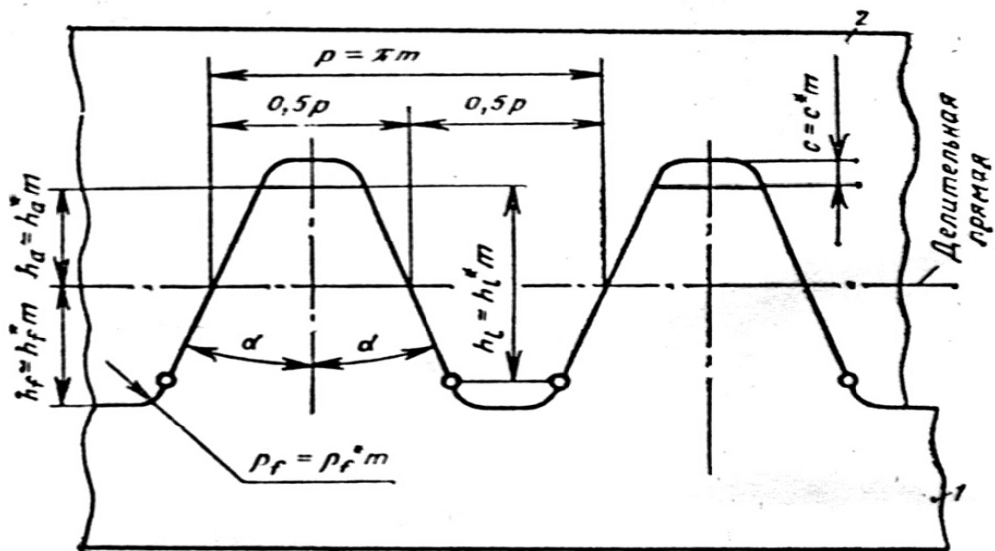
Исходный контур для цилиндрической зубчатой передачи
